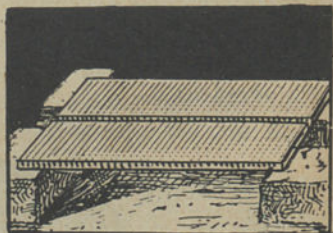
O avêso da linha de soldadura deve estar completamente livre.
